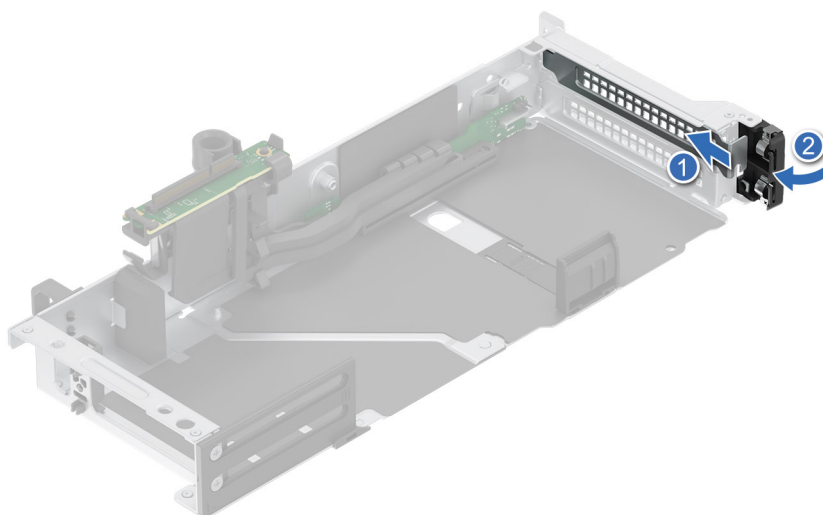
Installation de la plaque de recouvrement métallique (carte de montage 4)
